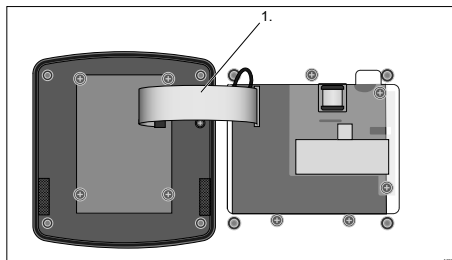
Staccare il cavo piatto multipolare dall'attacco
